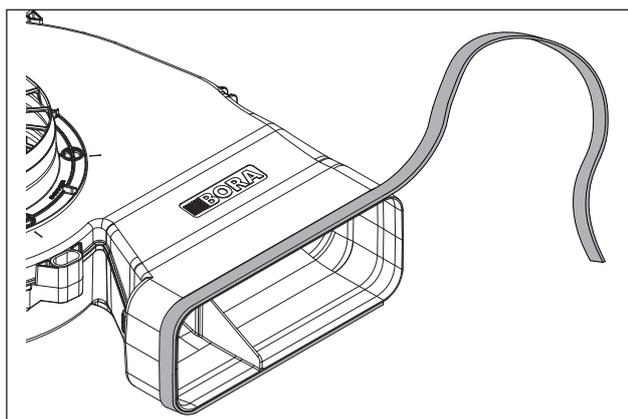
Position du joint pour montage avec pièce intermédiaire (gaine plate)
